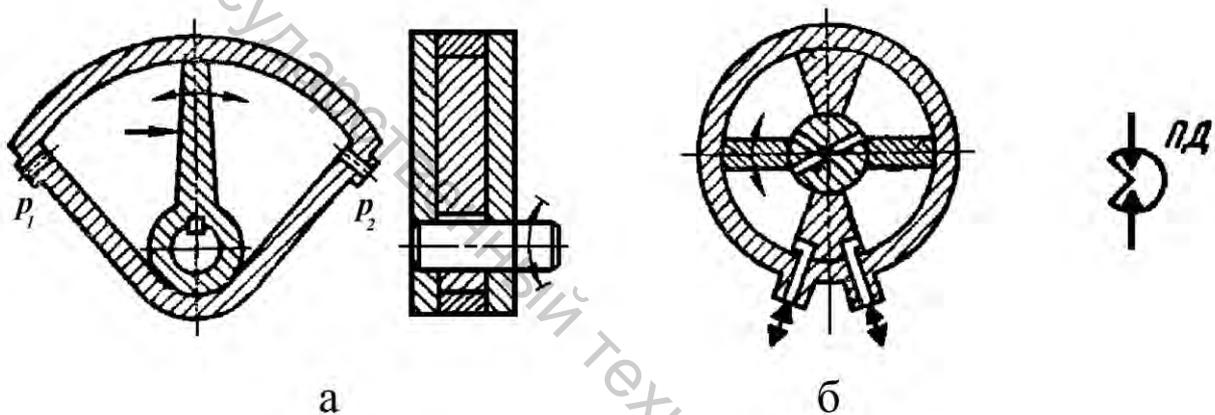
Пластинчатые поворотные гидродвигатели
